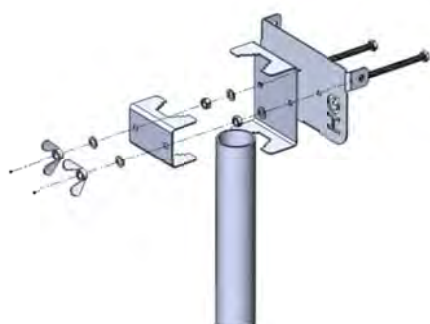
Монтажная схема сборки кронштейна и крепления корпусу излучателя
